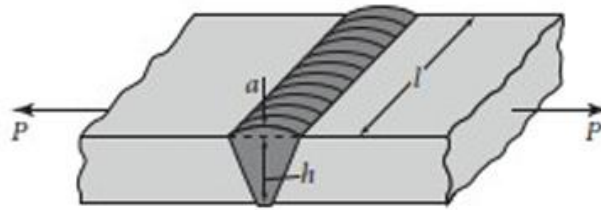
Soldadura a tope sometida a una carga axial
